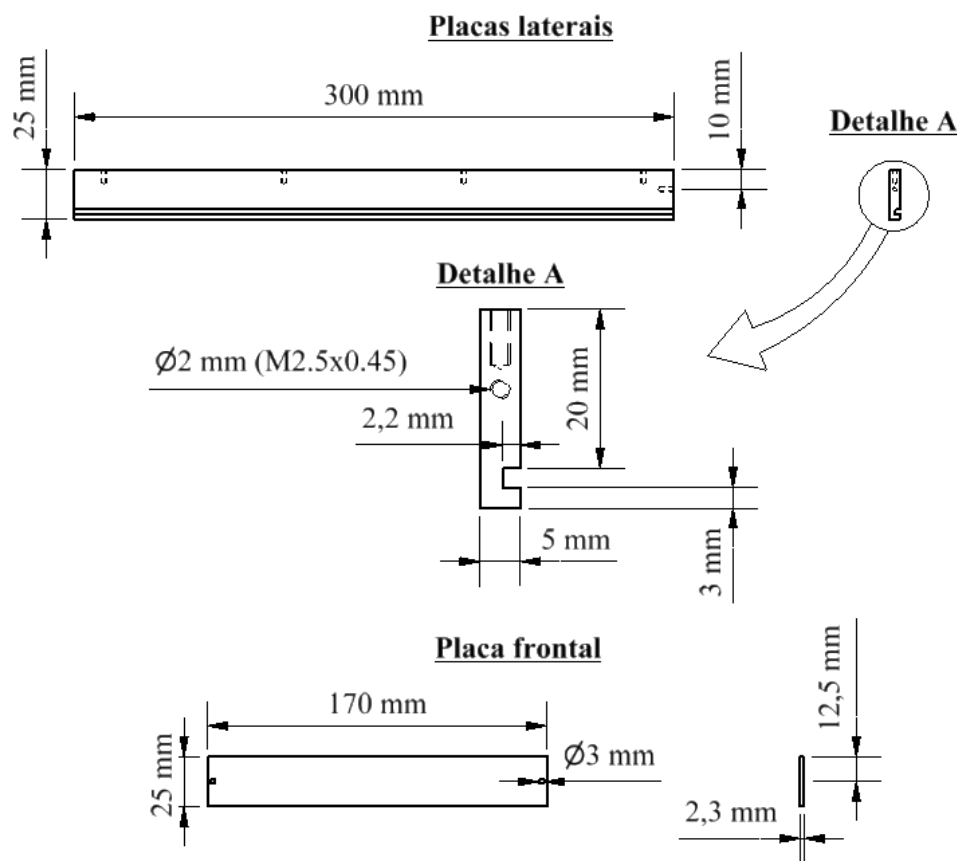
Dimensões e detalhamento das placas laterais e frontal.
